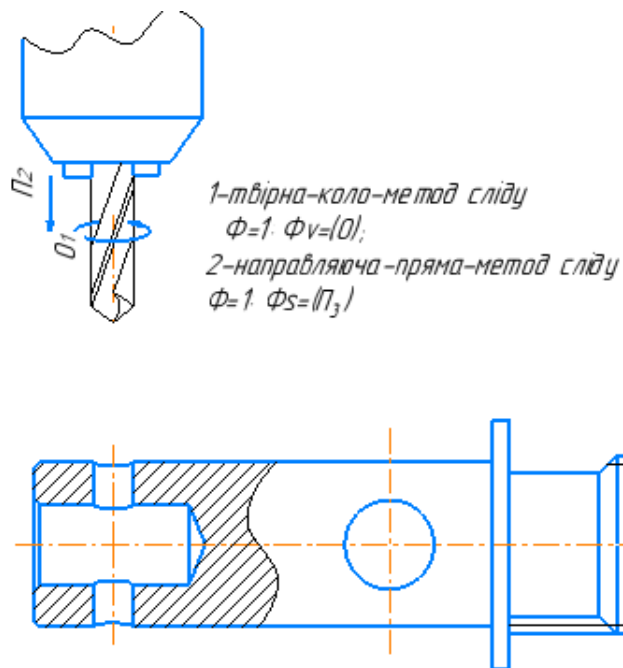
Обробка свердлами (основні формоутворюючі рухи)
